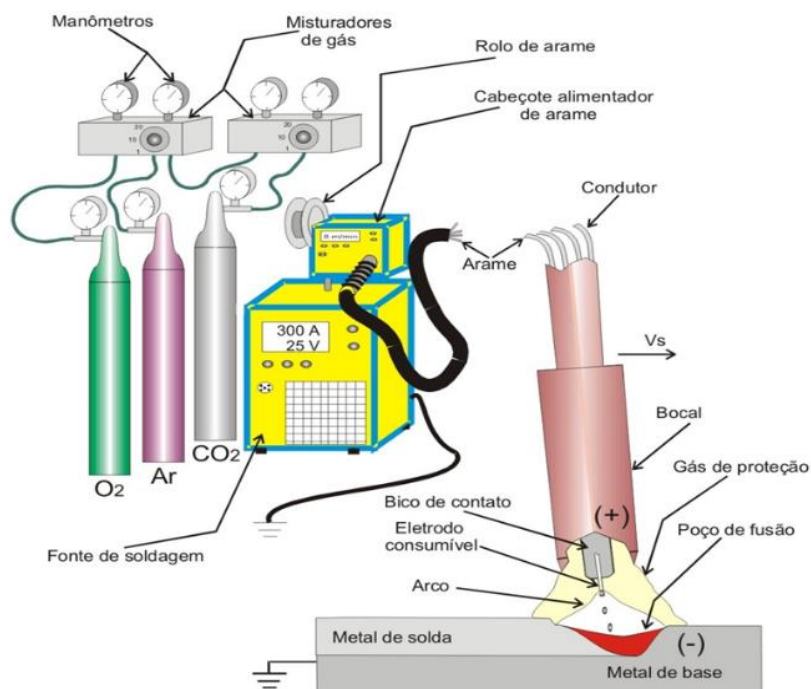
Equipamentos para soldagem MIG/MAG.
